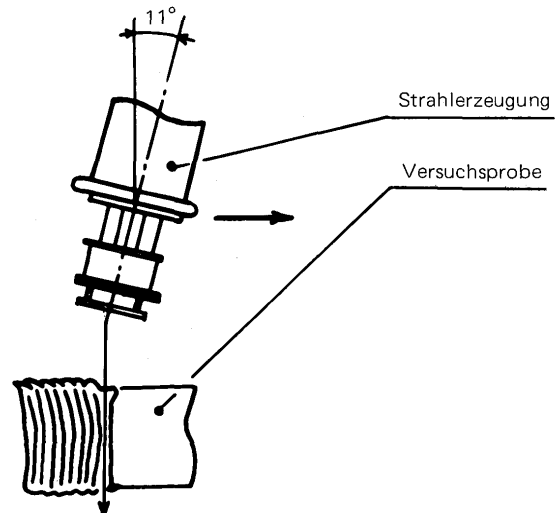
Schweißverfahren mit abgelenkten Elektronenstrahl
